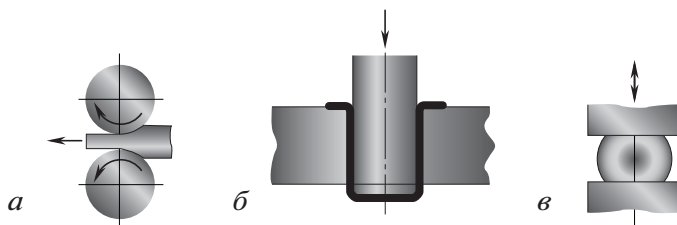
Обработка металлов давлением: *а* — прокатка; *б* — листовая штамповка; *в* — ковка
